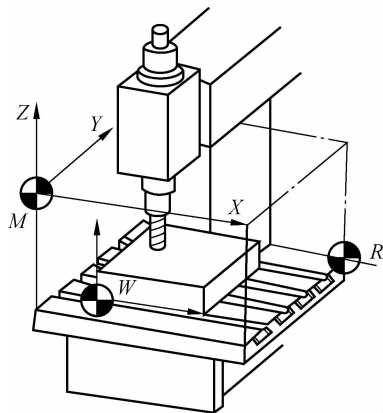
数控铣床的机床原点、机床参考点和工件原点示意
